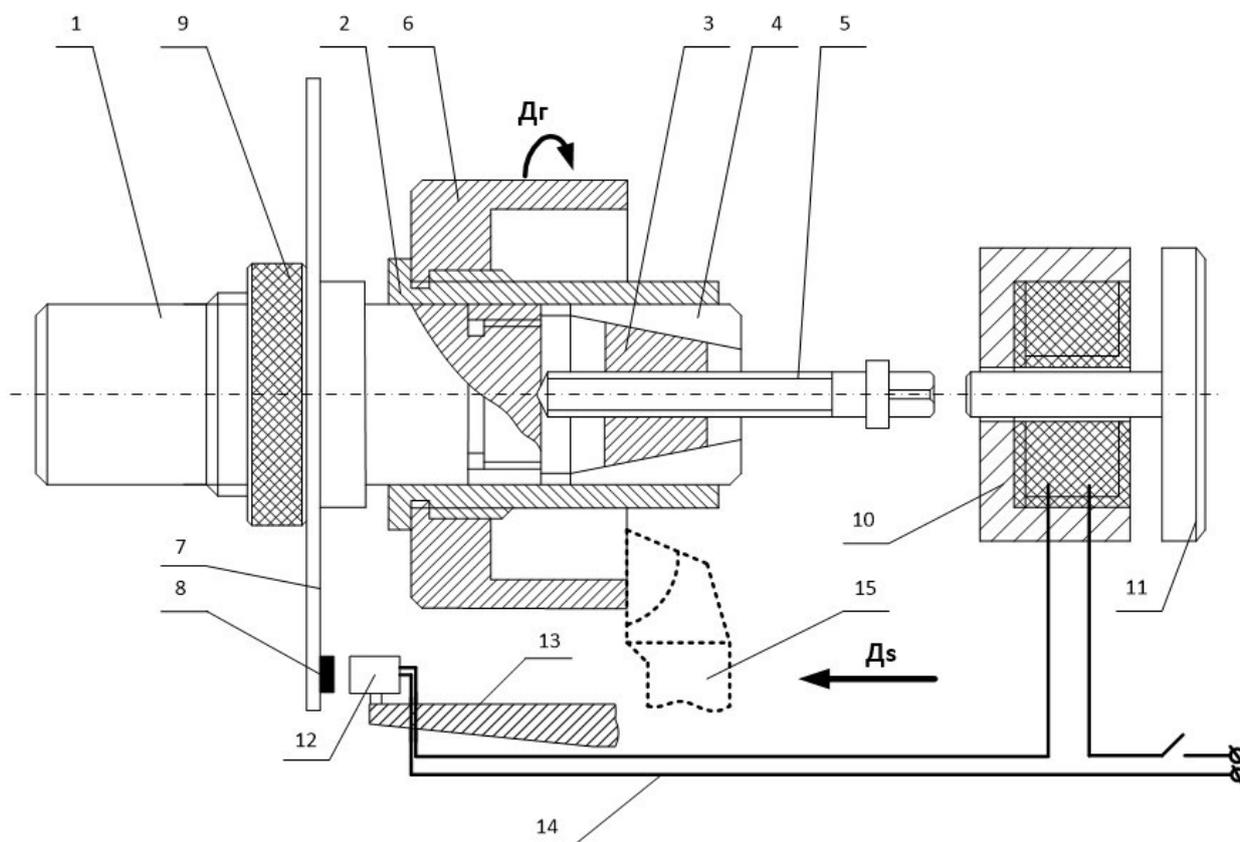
Цанговое приспособление для мгновенного прекращения резания: 1- корпус; 2 — втулка; 3 — конус; 4 — цанга; 5 — винт; 6 — образец; 7 — диск; 8 — магнит постоянный; 9 — контргайка; 10 — электромагнит; 11 — сердечник электромагнита; 12 — геркон; 13 — штанга; 14 — электрическая цепь; 15 — резец.
